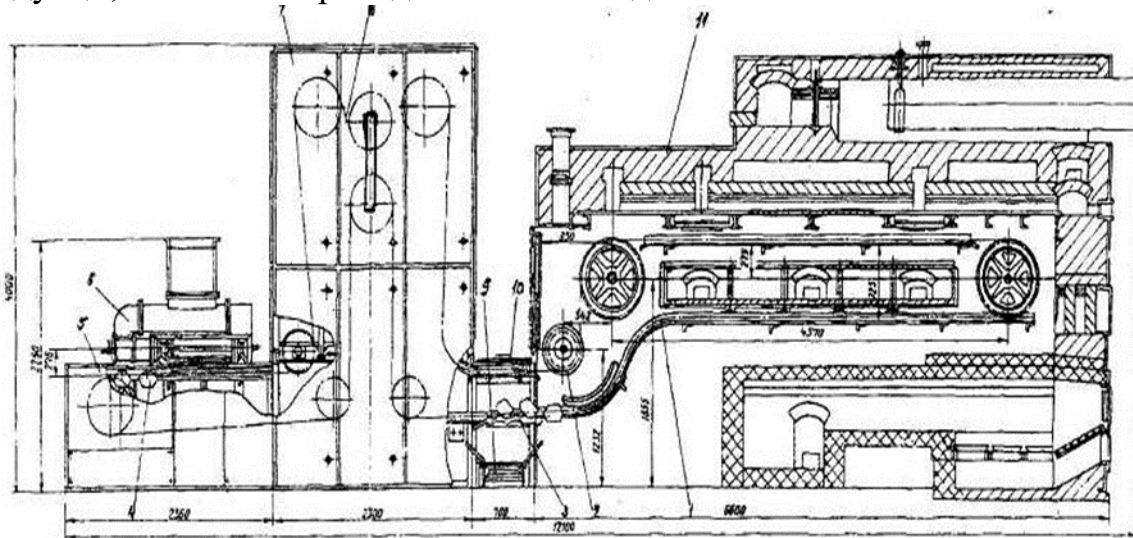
Вистійно-пічний агрегат П6-ХРМ
